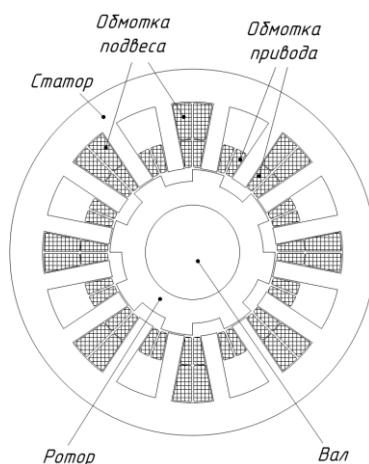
Разрез бесподшипниковой индукторной машины
